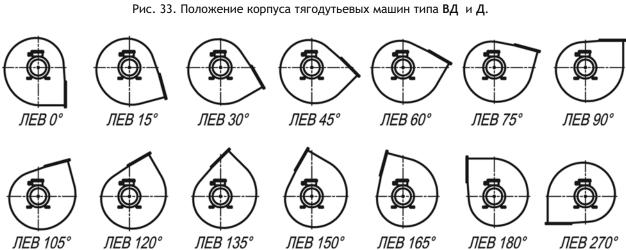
Положение корпуса тягодутьевых машин типа ВД и Д (ЛЕВ).
